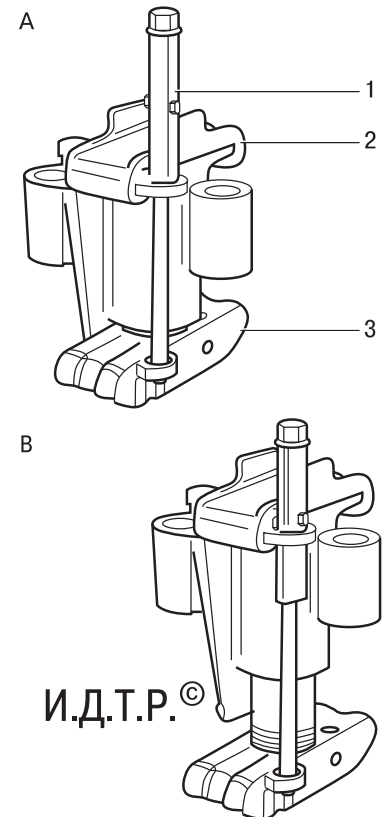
Фиксация и ослабление гидравлического натяжителя цепи привода газораспределительного механизма: А – натяжитель цепи зафиксирован; В – натяжитель цепи ослаблен; 1 – стопорный штифт; 2 – верхняя направляющая цепи; 3 – нижняя направляющая цепи
